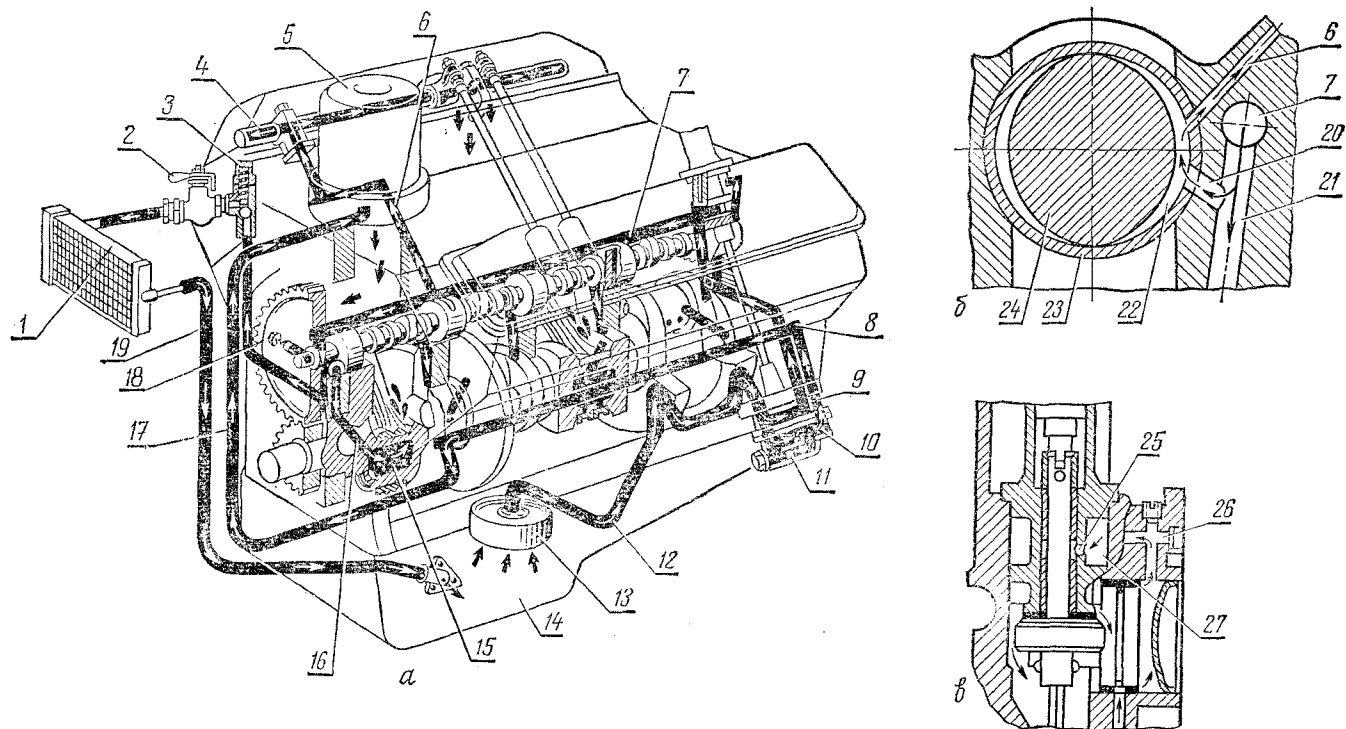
Схема системы смазки двигателя ГАЗ-53:
